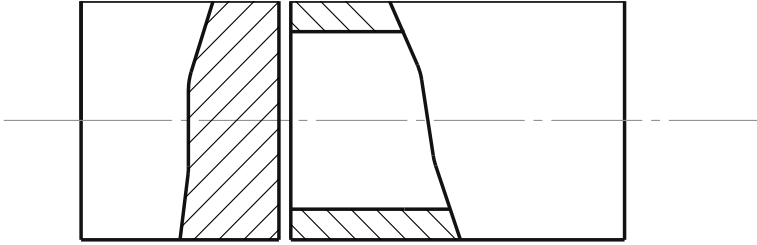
Сварка трубы со стержнем встык
